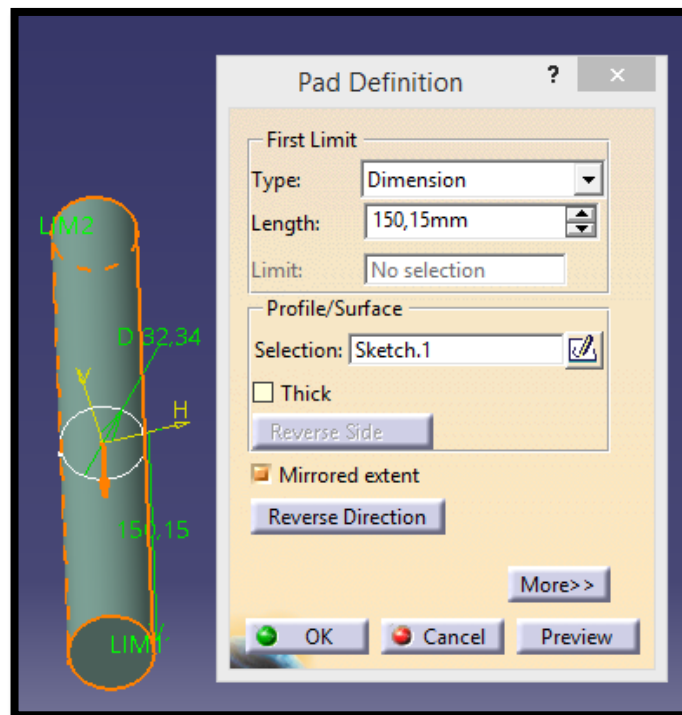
Seat mounting frame 11: Pad barra inferior 2
